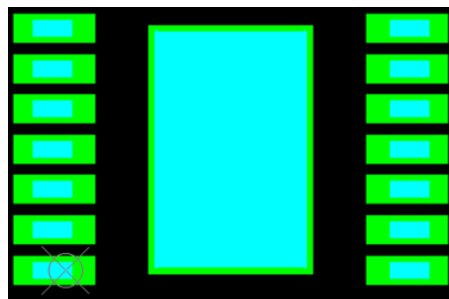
SO-14 PCB 焊盘上的 PWP0014L，浅蓝色：PWP0014L 引线，绿色：其他 SO-14 PCB 焊盘
